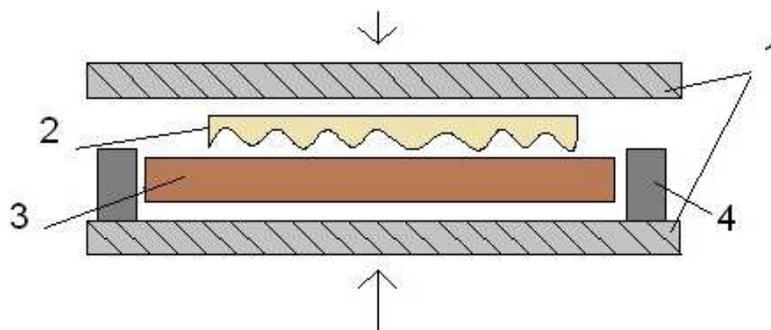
Формирование пакета для прессования: 1 – плиты пресса; 2 – пуансон; 3 – заготовленная деталь древесины; 4 – стальные пластины
